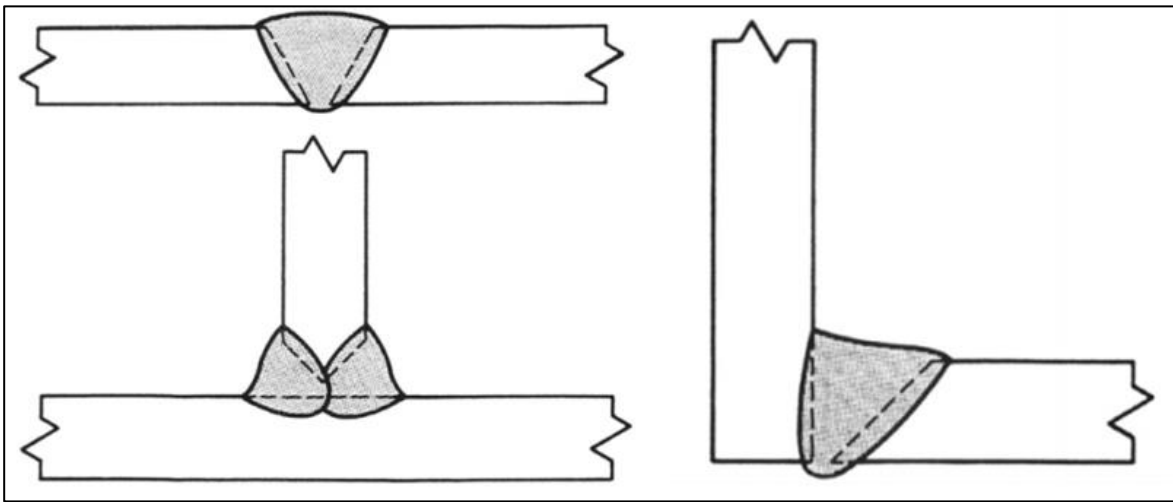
Ejemplos De Soldaduras En Juntas Con Penetración Completa [3].
